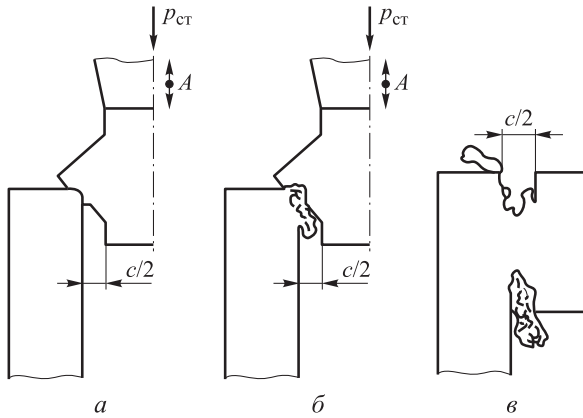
Схема механизма образования СС при УЗС впрессовкой фигурного СЭ
